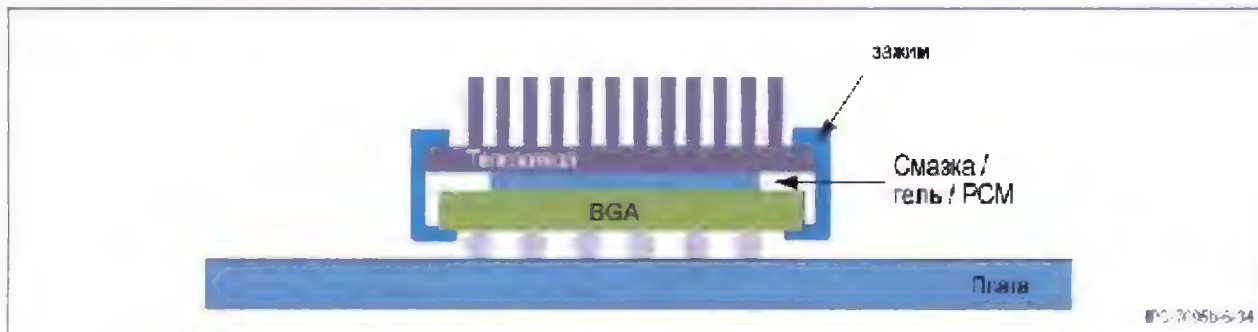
Радиатор, установленный на корпус BGA при помощи зажимов, крепящихся к подложке компонента
